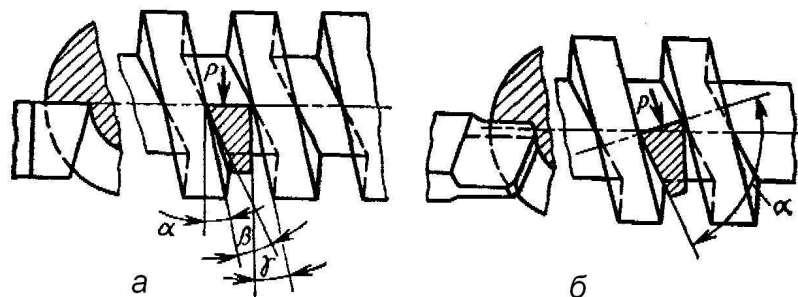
Схемы установки резцов при нарезании резьбы
